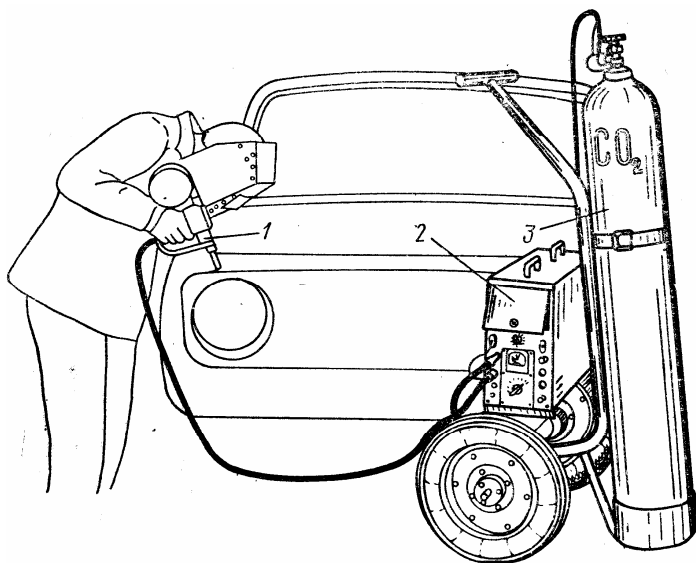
Сварка кузова с помощью полуавтоматической установки:
